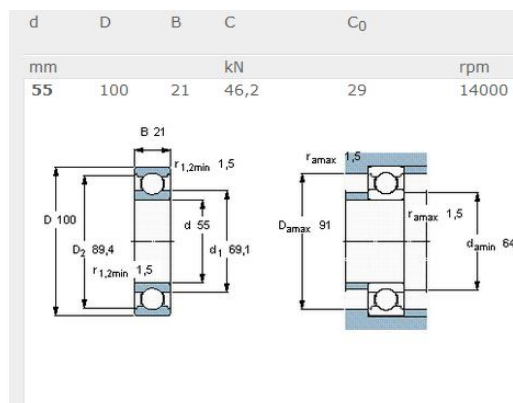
DIMENSIONES GENERALES DEL RODAMIENTO 6211
